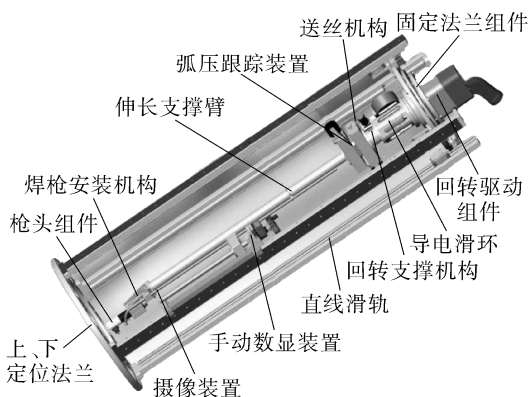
斜 45° 全位置自动焊接设备结构示意图
